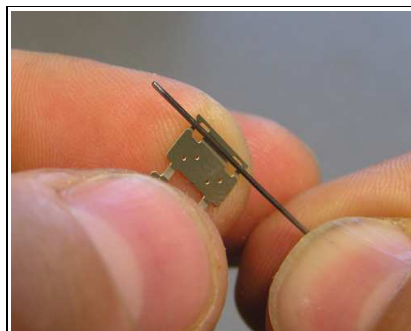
Hilfswerkzeug 0,6mm Stahldraht in die Ätznut legen.
